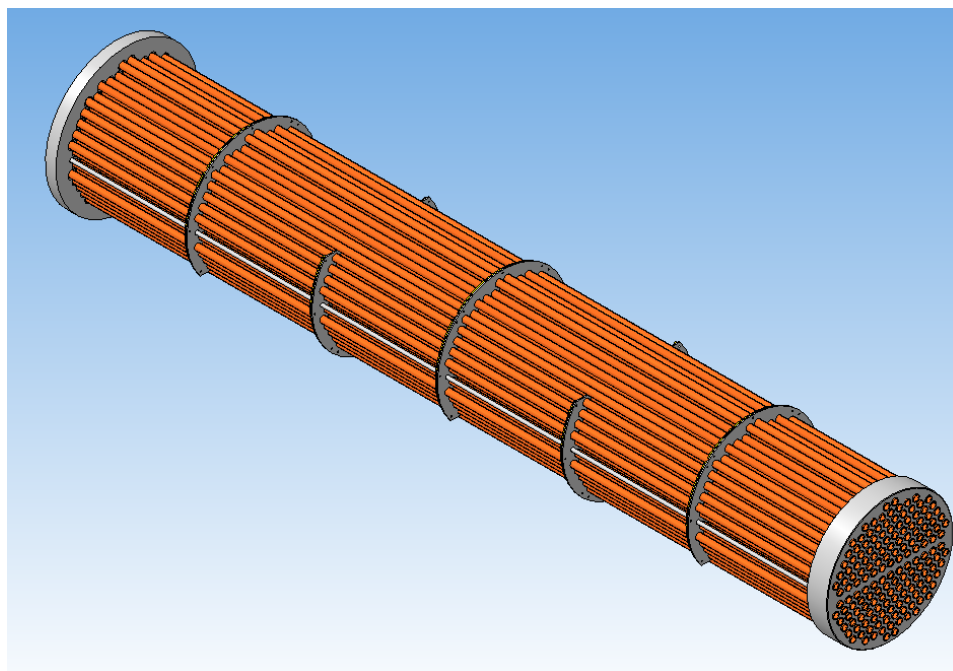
Загальний вигляд трубного пучка з сегментними діафрагмами
